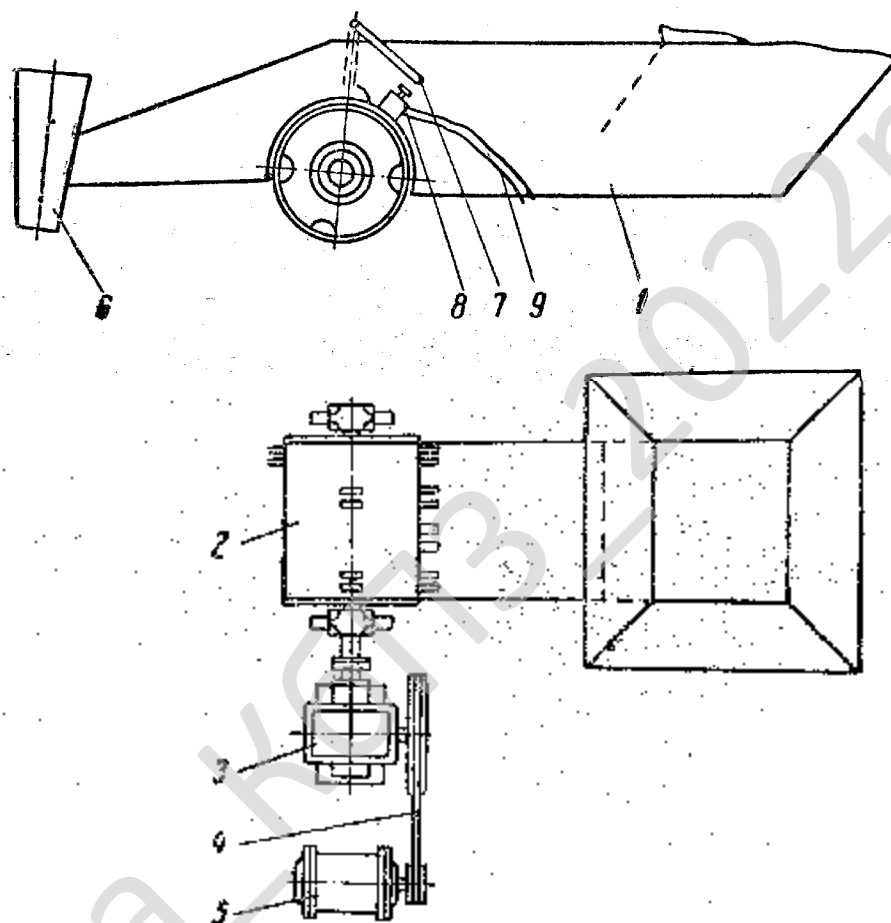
Схема живильника млина однорозмірними кулями
